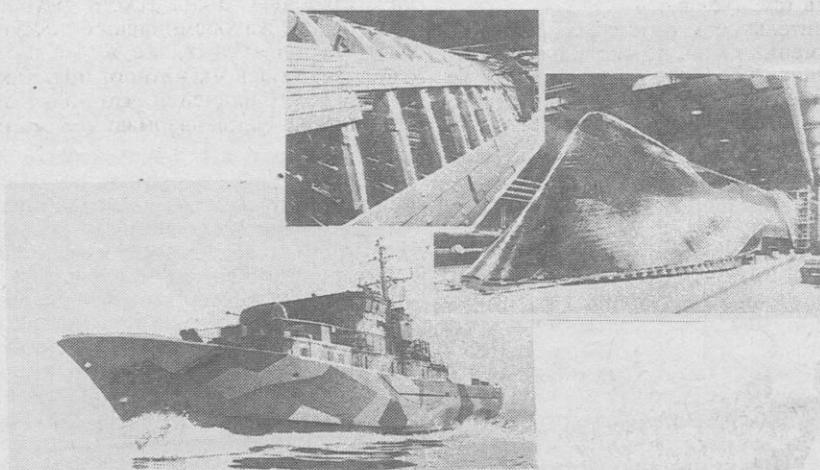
Этапы сборки корпуса тральщика – искателя мин типа «Ландсорт»
